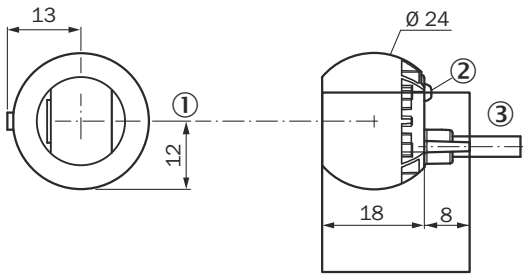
ZSE18-3xxxx/ZTx18-Cxxxx
